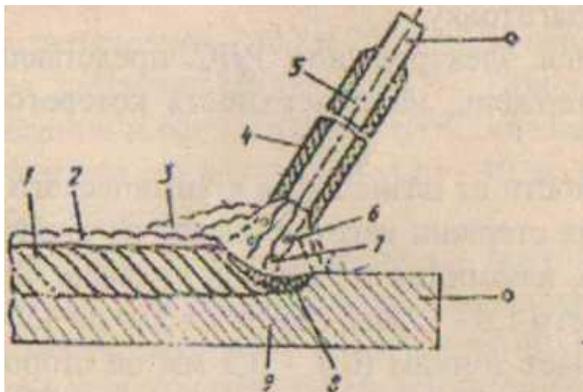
Ручная дуговая сварка покрытым электродом: 1 - сварной шов; 2 - шлаковая корка; 3 - защитная газовая атмосфера; 4 - электродное покрытие;
